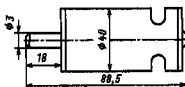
19 Габаритные и установочные размеры двигателей ДСР
